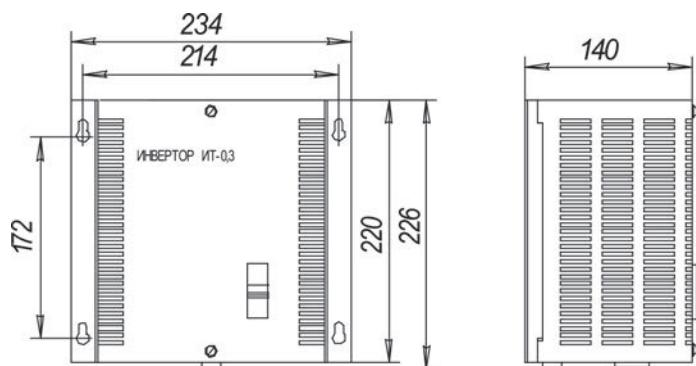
Габаритный чертеж инвертора ИТ-0,3
